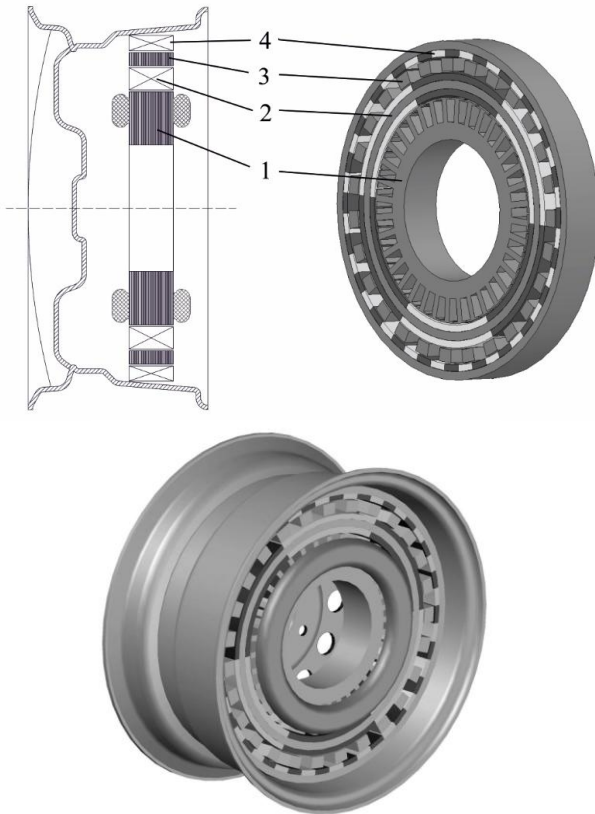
Схема размещения электродвигателя с магнитным редуктором в автомобильном диске R16.
